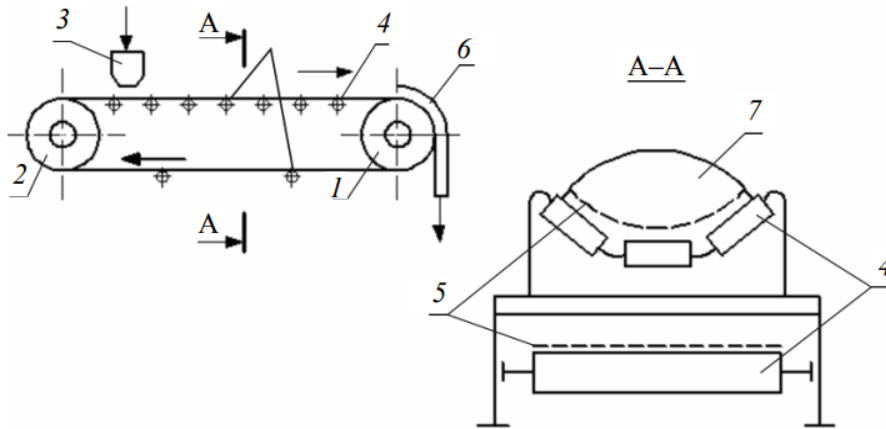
Схема пристрою стрічкового транспортера:
